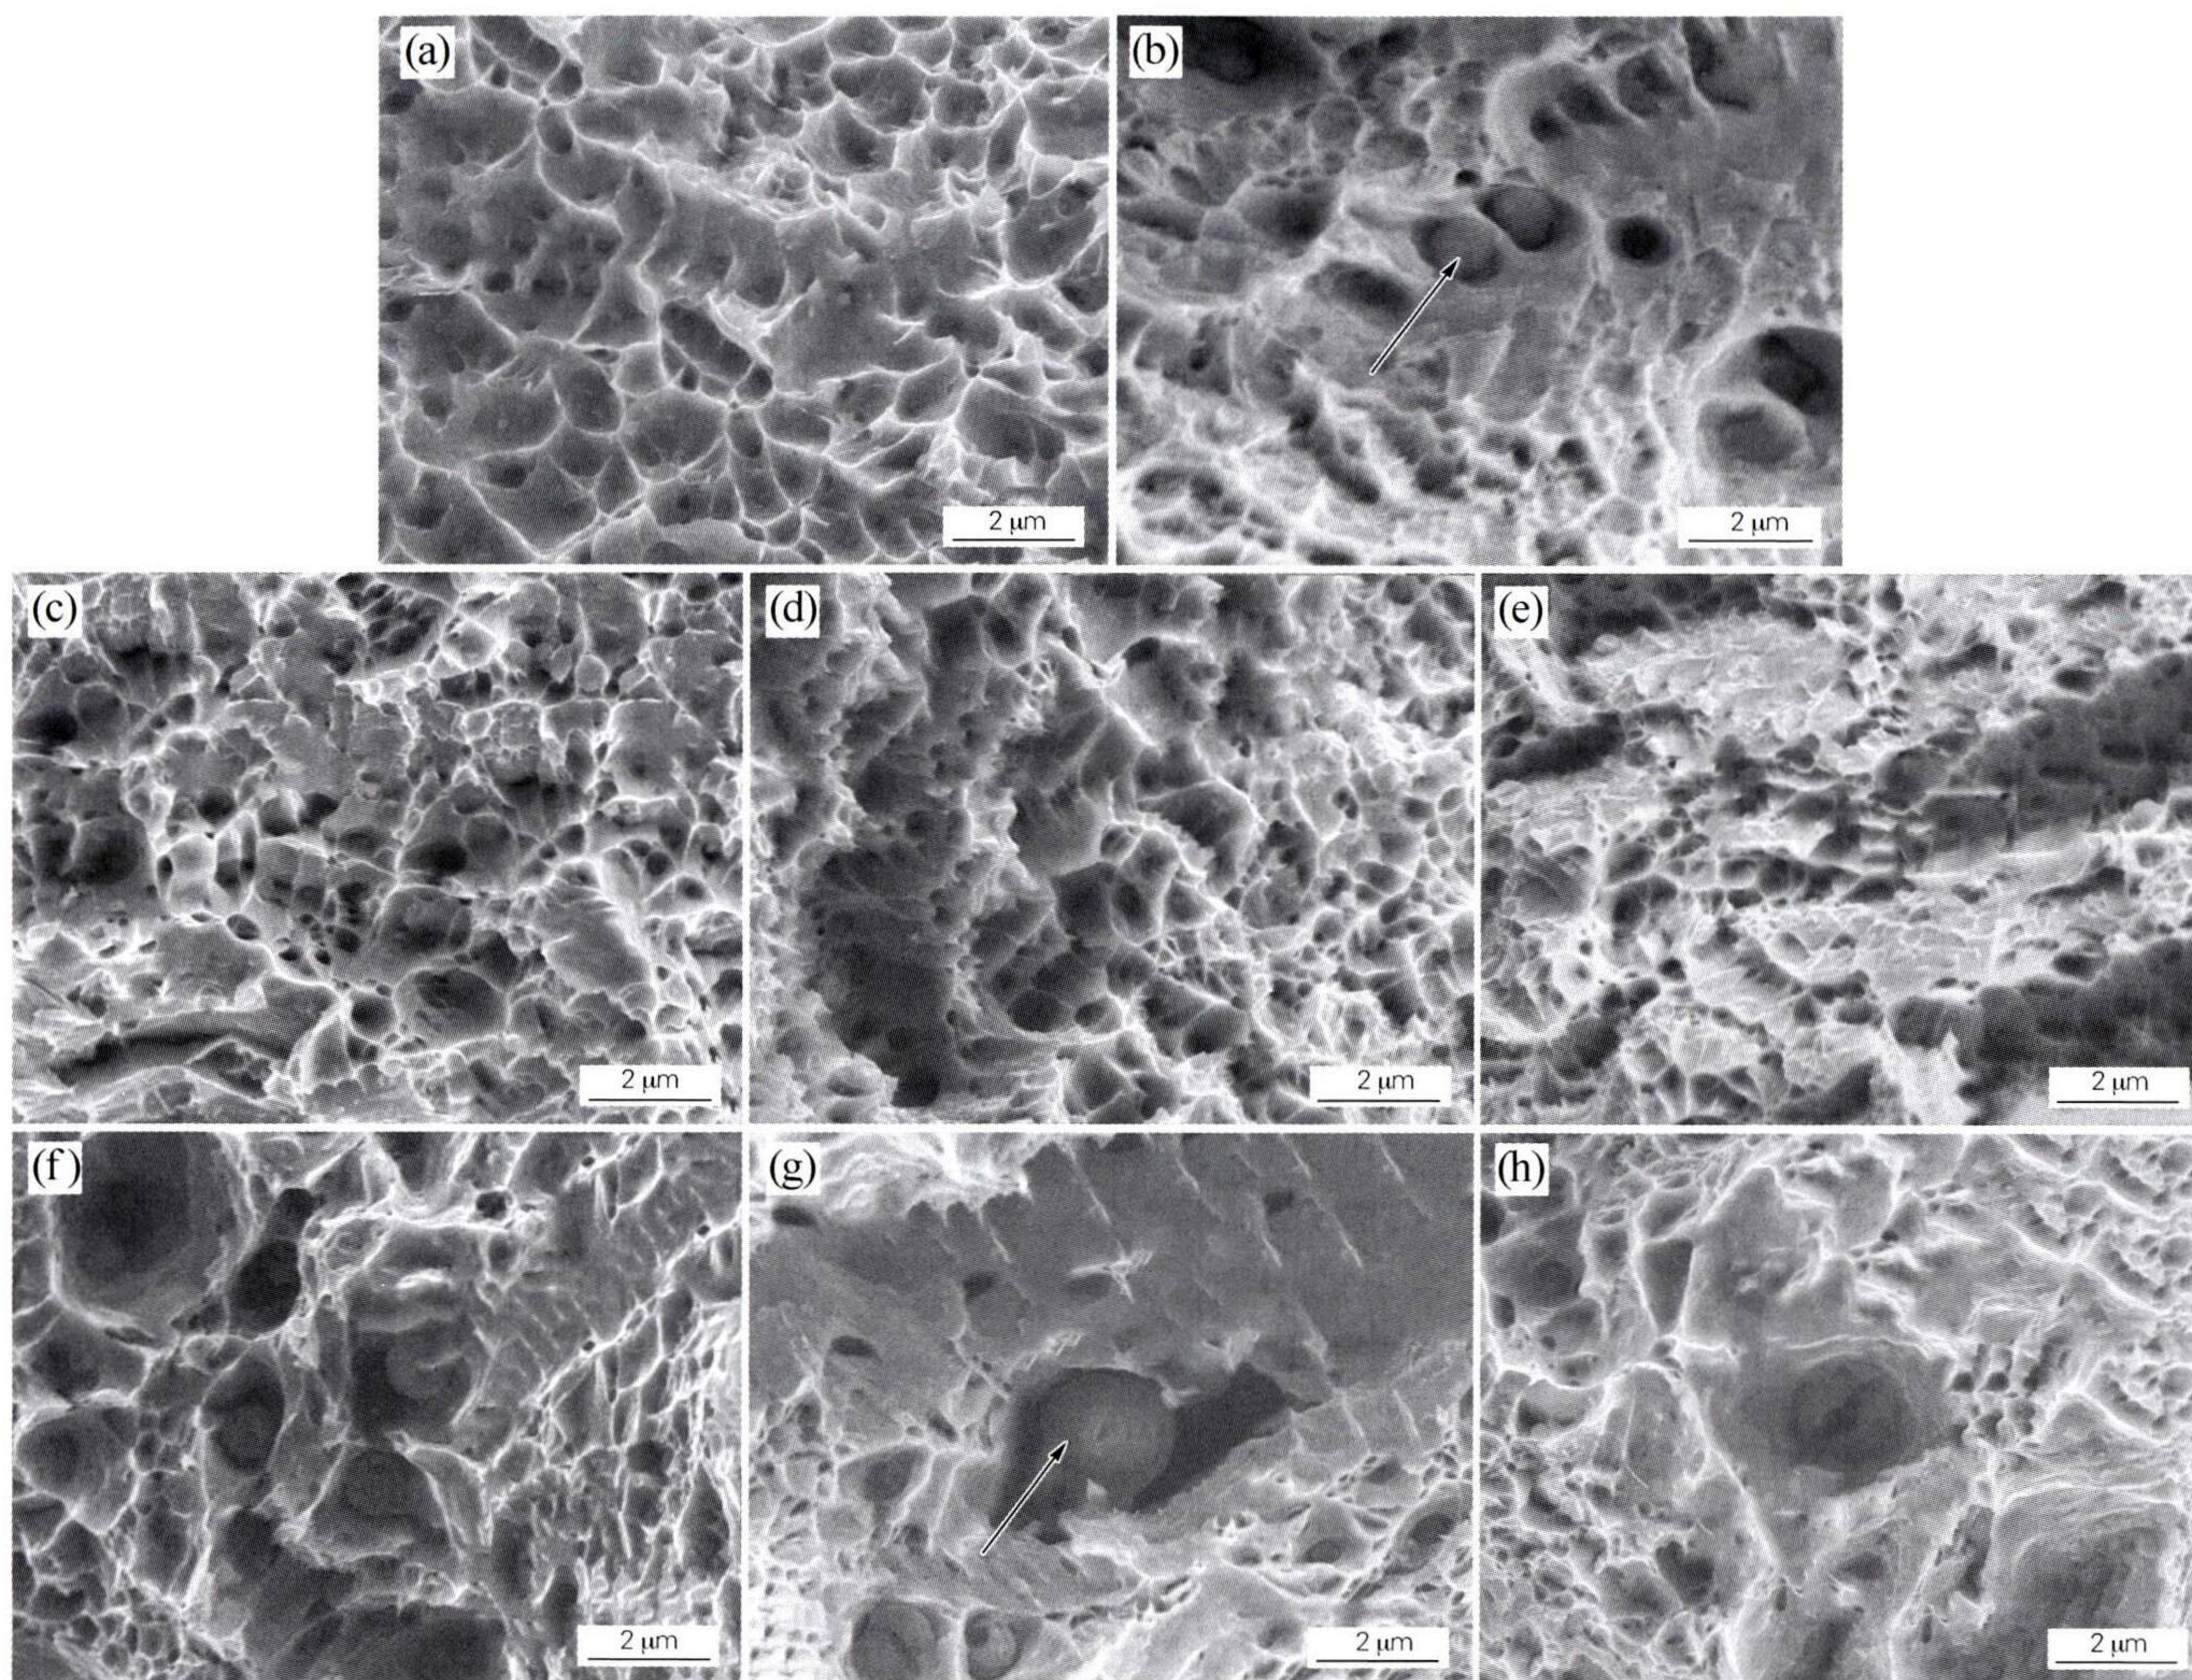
母材及不同热处理条件下焊接接头冲击断口形貌
